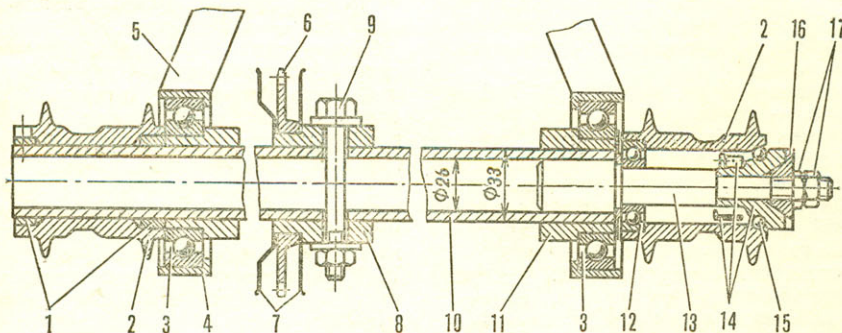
Ходовой вал: 1 — посадочные кольца, 2 — ступица (от дорожного велосипеда), 3 — подшипник, 4 — обойма подшипника, 5 — тяга, 6 — ведомая звездочка, 7 — защитные шайбы, 8 — втулка, 9 — болт крепления, 10 — вал, 11 — втулка подшипника, 12 — опорный подшипник, 13 — палец ходового вала, 14 — детали обгонной муфты, 15 — радиально-упорный подшипник, 16 — конусная шайба, 17 — гайка и контргайка.
